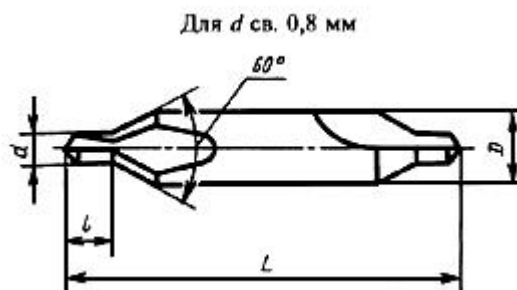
Сверло 2317-0007 ГОСТ 14952-75 тип А
